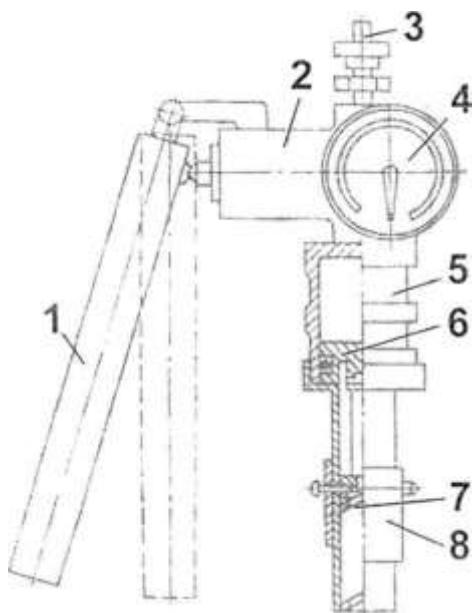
Пристрій КИ-9917: 1 – важіль; 2 – корпус; 3 – паливо провід високого тиску; 4 – манометр; 5 – резервуар для палива; 6 – поршень; 7 – пружина; 8 – ручка резервуара.
